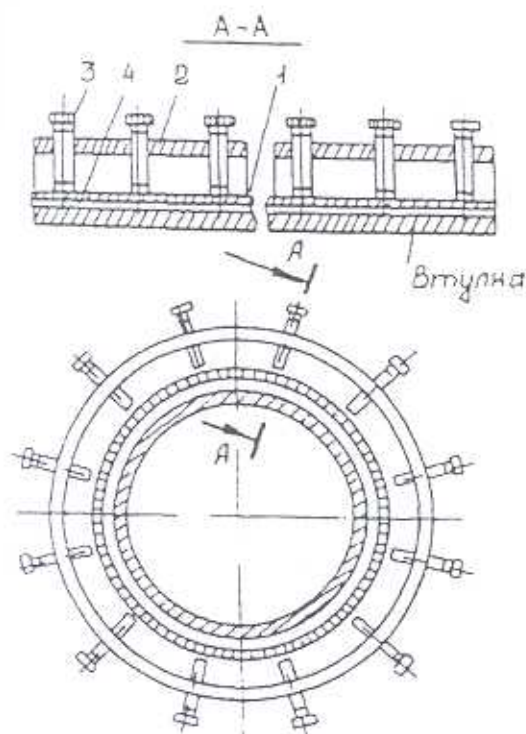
Приспособление для опрессовки изоляции втулки:
